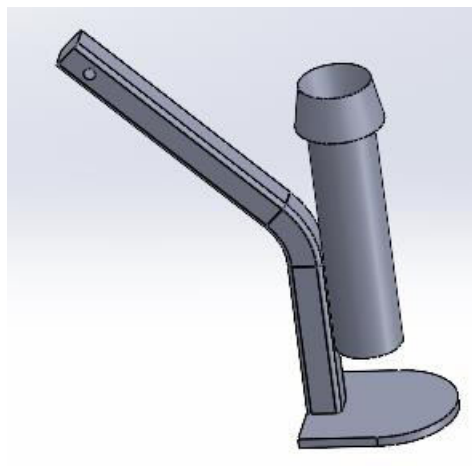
Ensamblaje final del brazo para la aplicación en cobertera.
